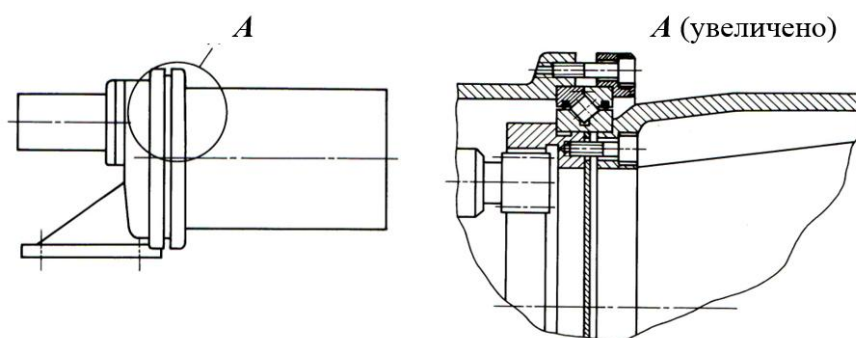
Схема привода барабана ленточного транспортера одноступенчатым цилиндрическим мотор-редуктором с внутренним зацеплением
